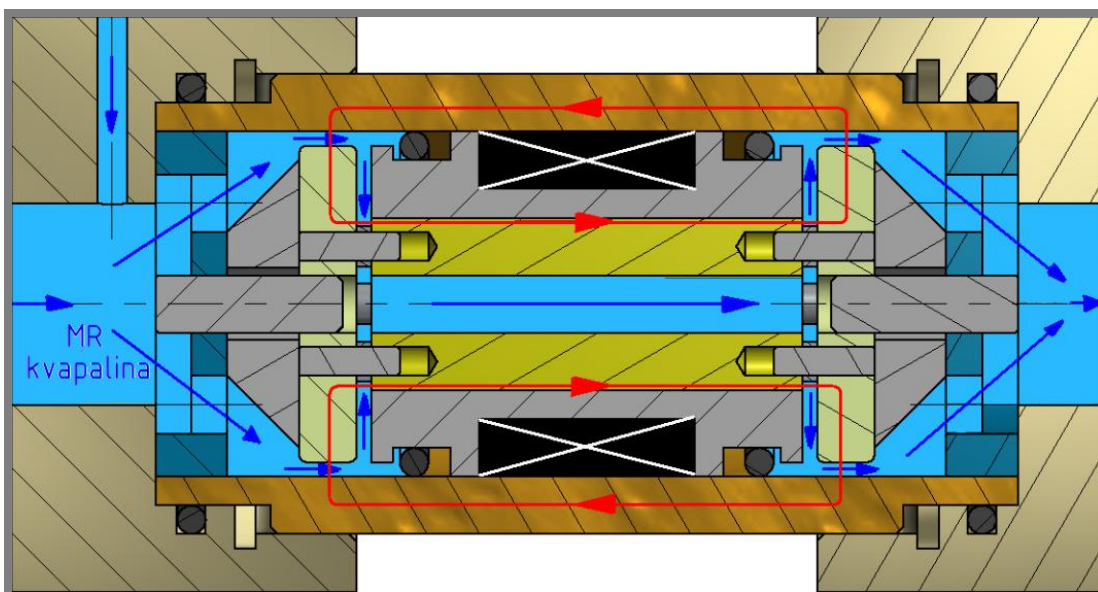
MR ventil s radiálnou a medzikruhovou štrbinou
